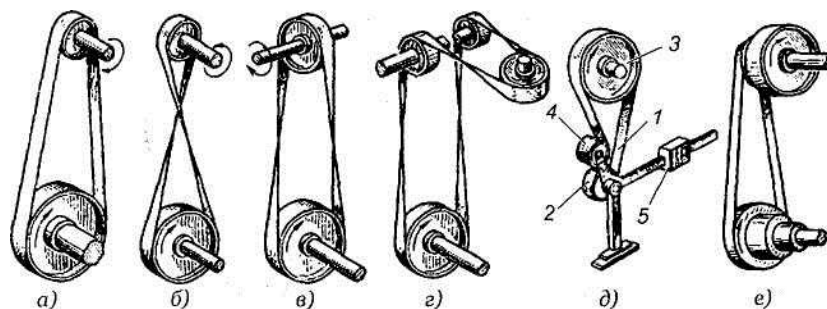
Виды ременных передач: а — открытая передача; б — перекрестная передача; в — полуперекрестная передача (со скрещивающимися валами); г — угловая передача (с направляющим роликом); д — передача с нажимным роликом; е — передача со ступенчатым шкивом
